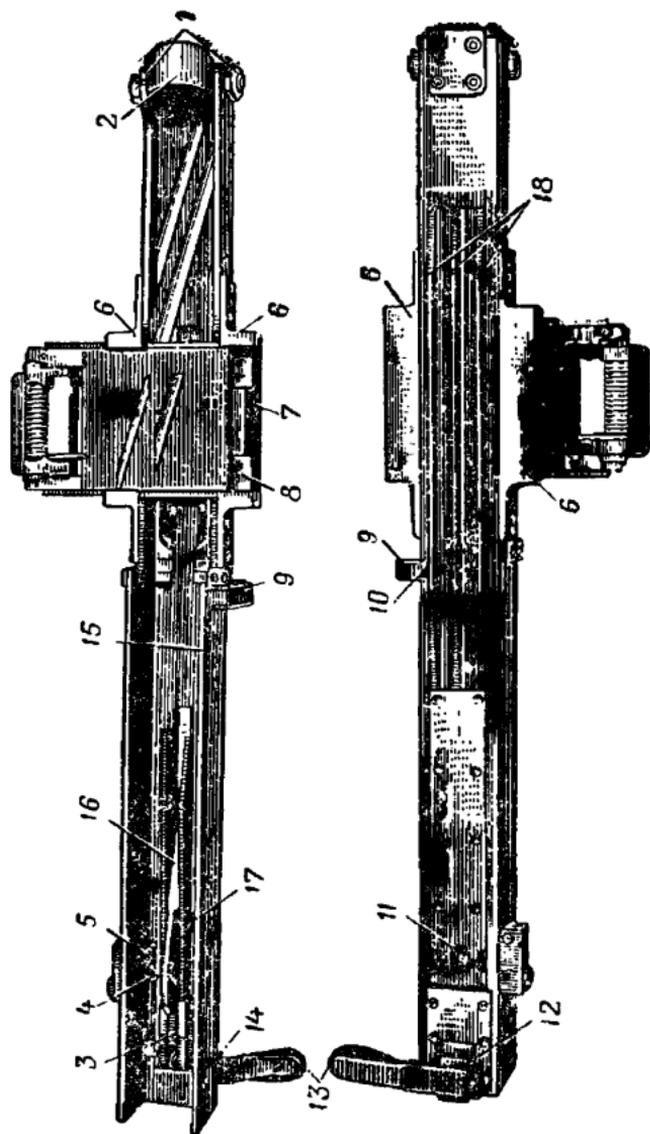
Крышка ствольной коробки (вид снизу и сверху):
